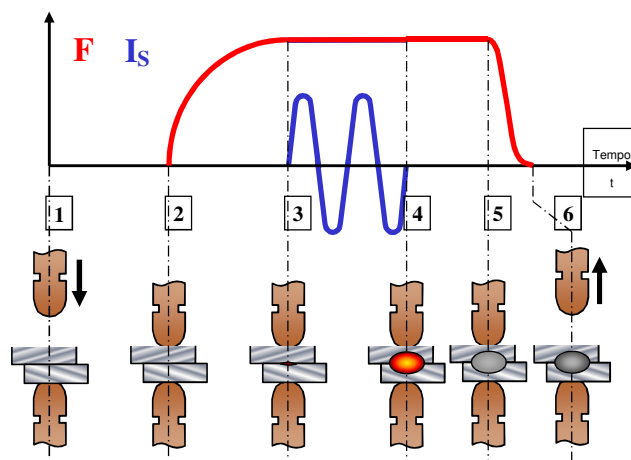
Processo de soldagem à resistência (SOLDAGEM À RESISTÊNCIA A PONTO, 2000).
